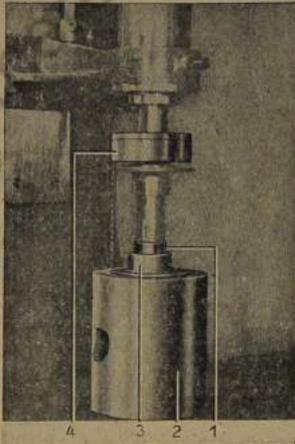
Laufbuchse zum Schrägrad für 4. Gang aufpressen
